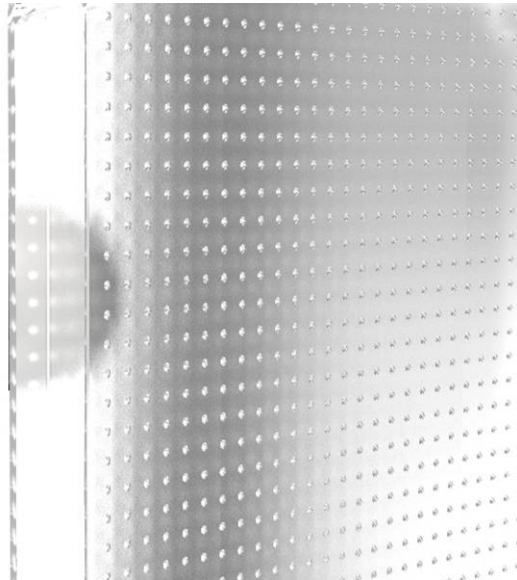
Schnitt durch die Definition des Lochdurchmessers für ein Probewerkzeug
